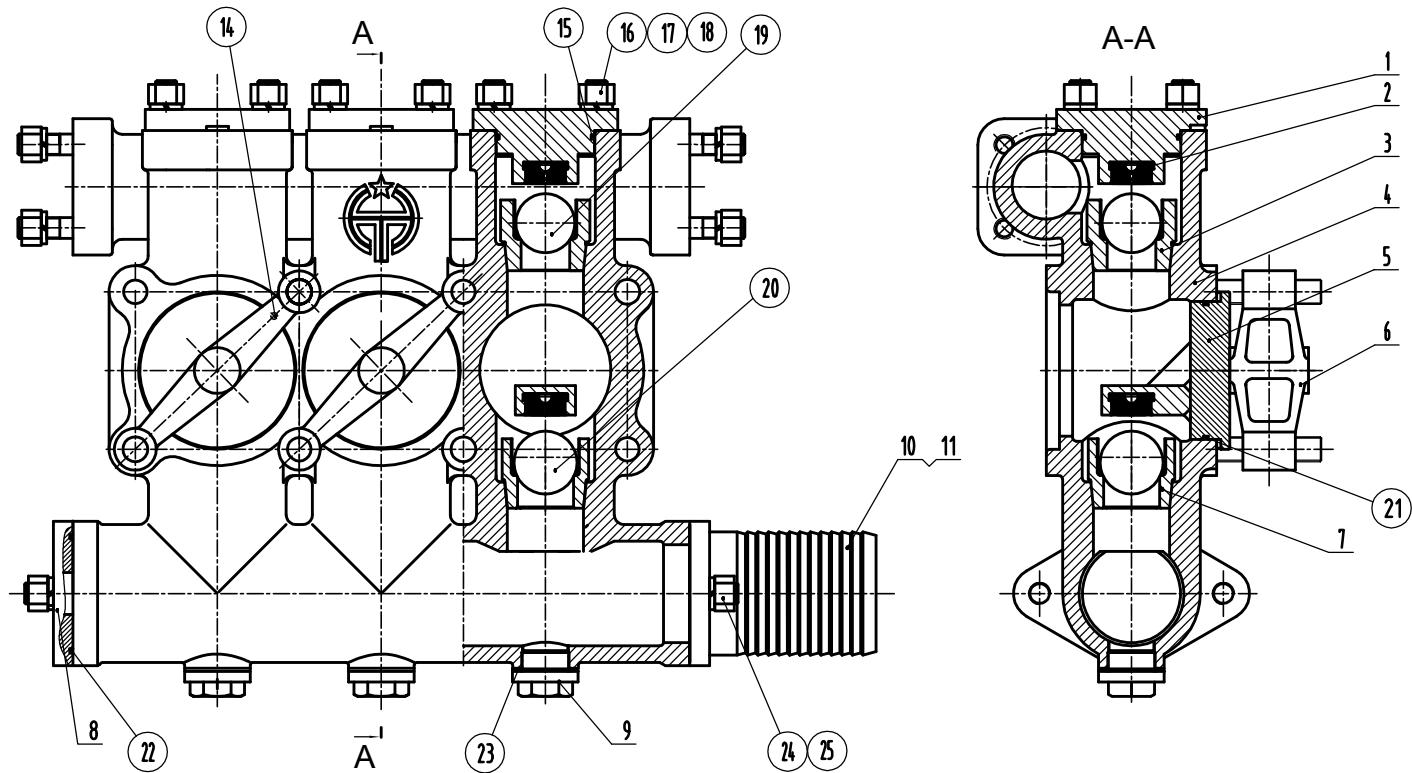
Корпус насоса BW600-02-00 (1)
